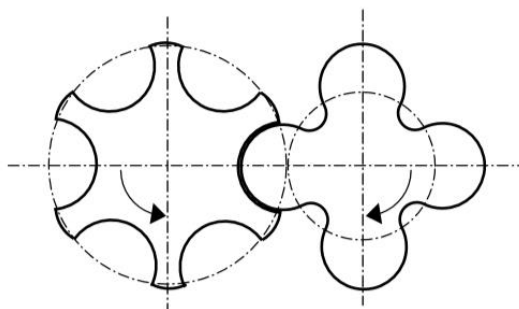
Rotores de um compressor parafuso duplo, corte transversal [1].
